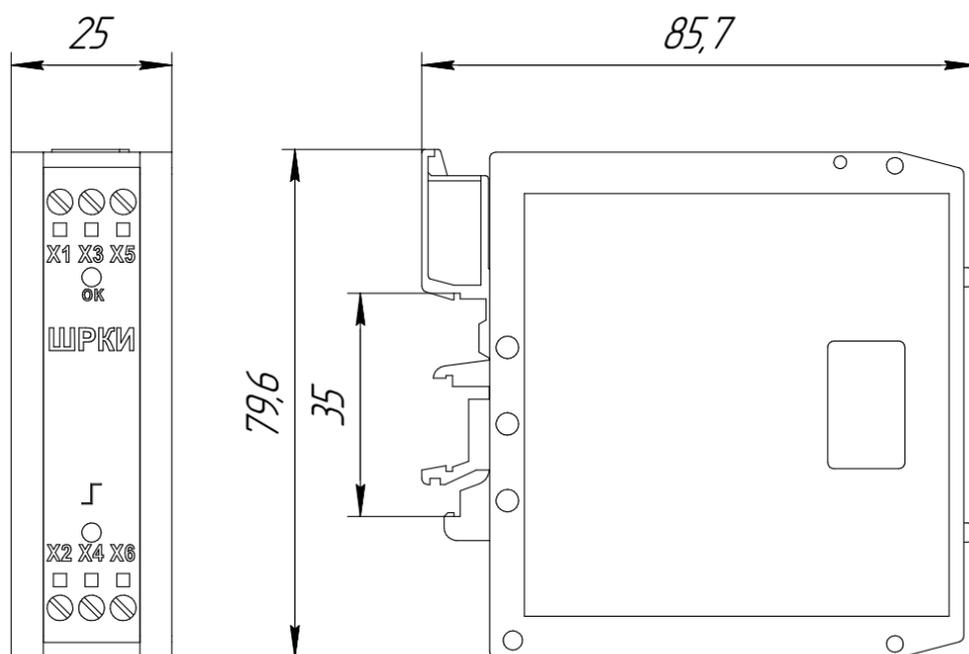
Габаритный чертеж ШРКИ-17
